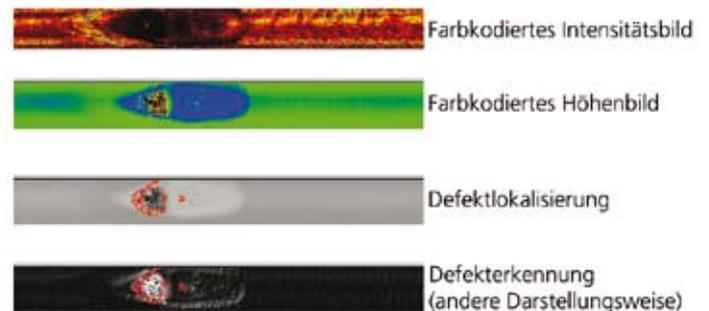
Schweißnaht, aufgenommen mit dem Sensor SISCAN MC64. Quelle: Siemens AG.
